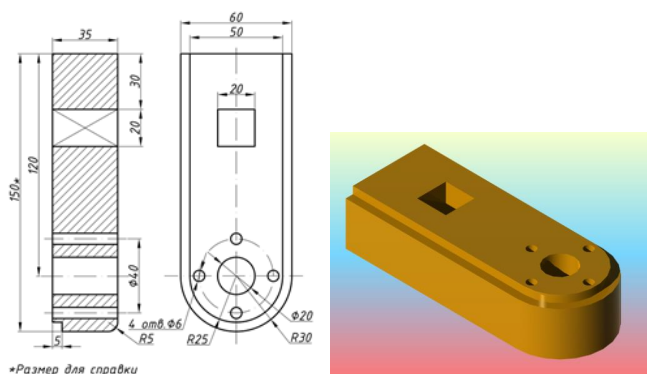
Разработка чертежа и твердотельной модели корпусной детали
